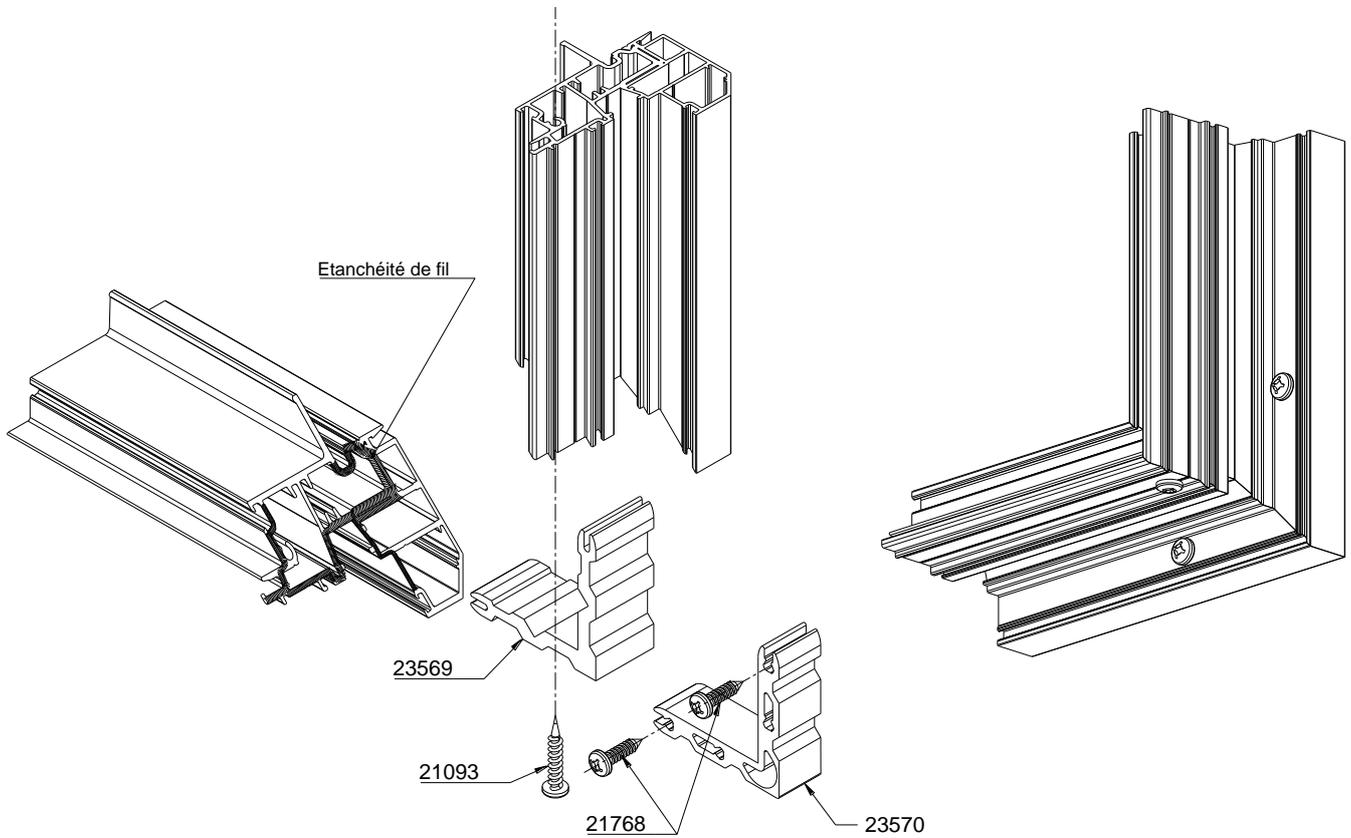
DETAILS D'ASSEMBLAGE ET ETANCHEITE SEUIL
